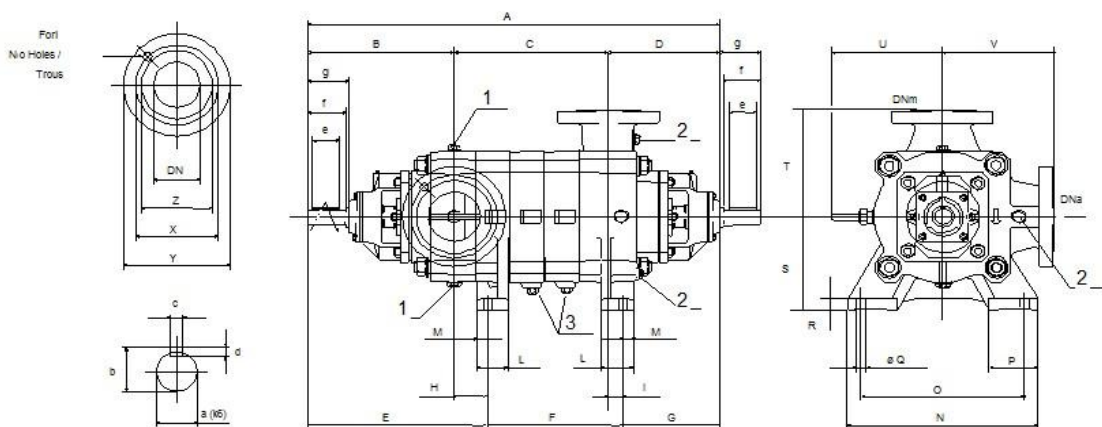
Dimensions de la pompe PM 100 / 2 C
